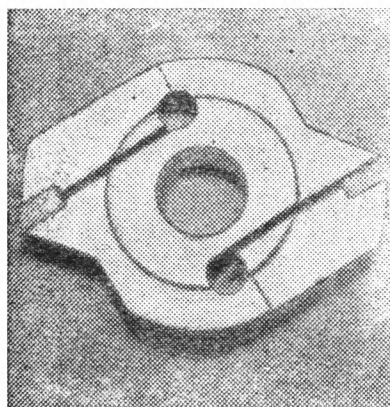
Двузубая фреза по дереву с керамическими пластинками.
